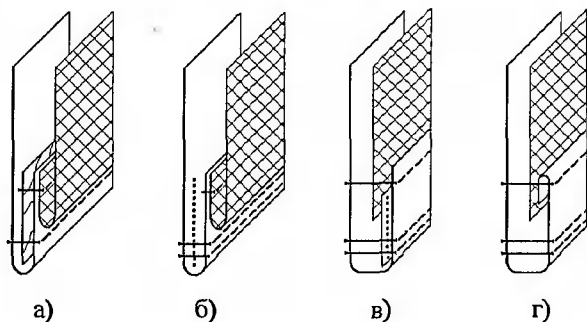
Обработка низа рукавов: а — с неклеевой прокладкой и притачиванием подкладки; б — с закреплением клеем и притачиванием подкладки; в — с клеевой прокладкой швом в подгибку с открытым срезом с настрачиванием припуска на подкладку; г — без прокладки швом в подгибку с закрытым срезом с настрачиванием припуска на подкладку
